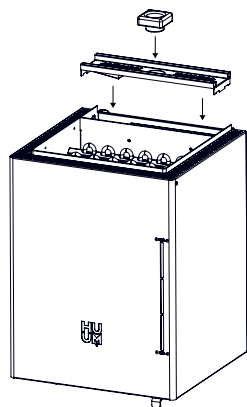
Instalace rozpěrky topných těles HUUM CORE Wall a CORE Wall Combi.
